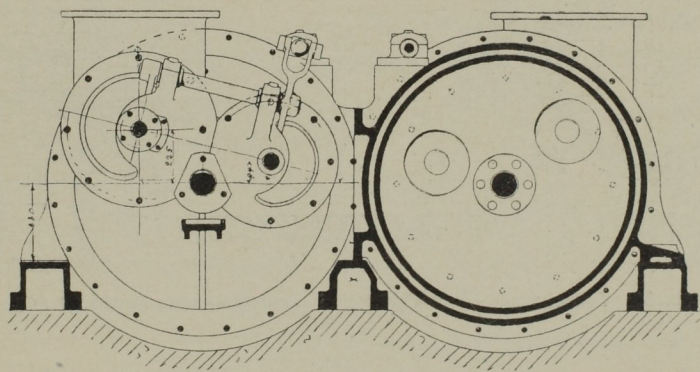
Stirnansicht und Querschnitt der Windcylinder.
